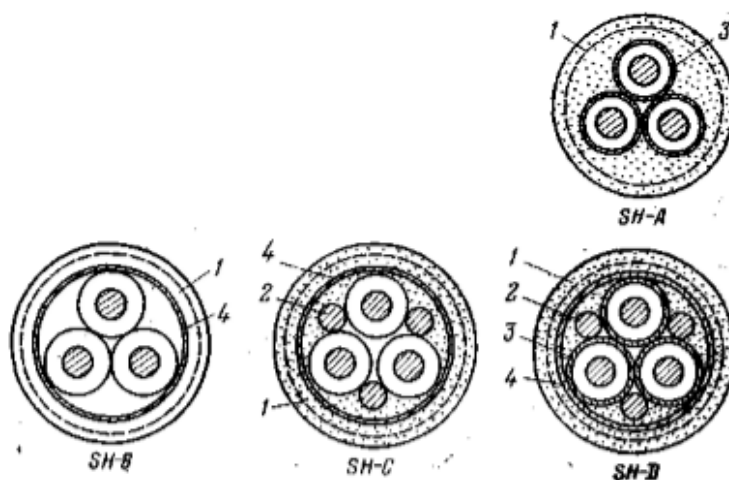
Конструкции высоковольтных гибких кабелей, выпускаемых в США: 1- упрочняющая оплётка; 2-заземляющая жила; 3- металлический экран по жиле в виде оплётки; 4-общий металлический экран в виде оплётки.
